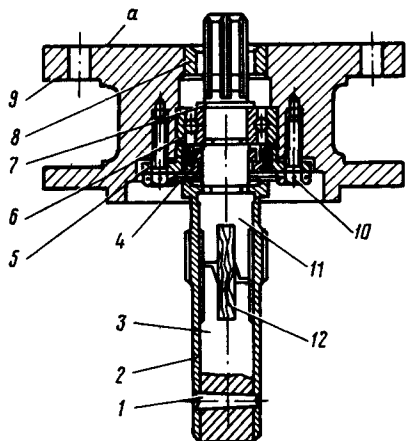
Нижний корпус регулятора дизеля 2Д100 с приводом:
